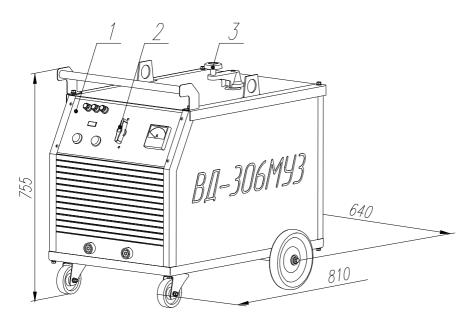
Общий вид выпрямителя сварочного
